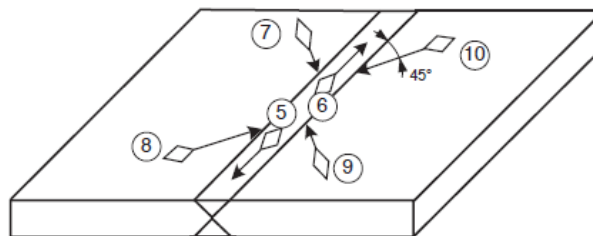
Ensayo en soldadura sin mecanizar
